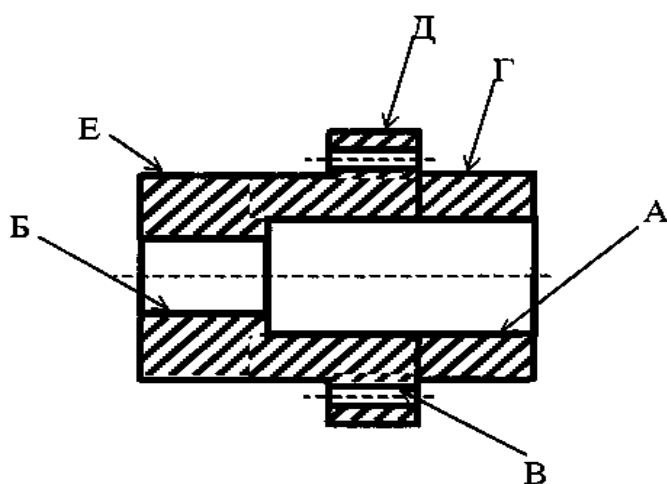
Эскиз детали с указанием заданных обозначений размеров и шероховатости поверхностей
